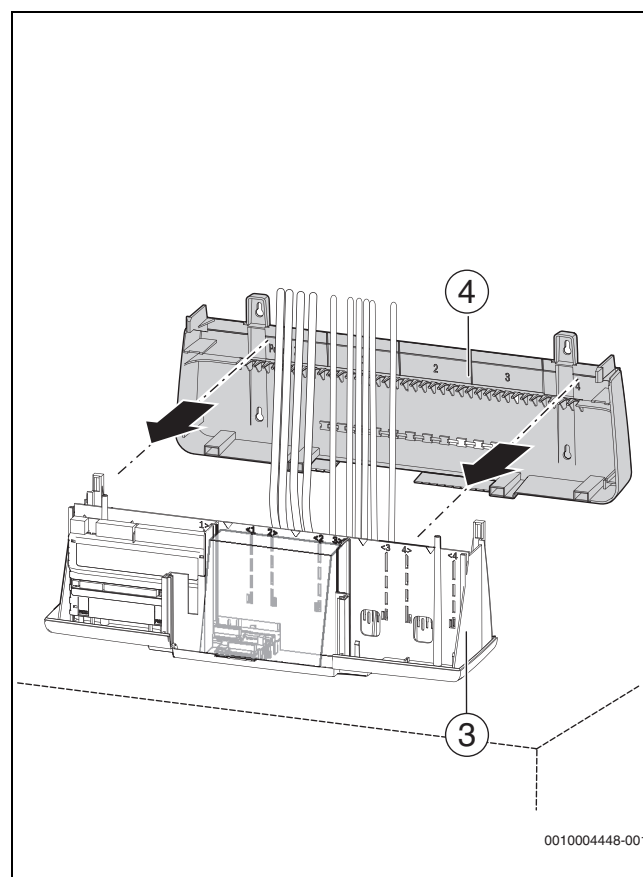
Insérer le montage dans la chaudière, enclencher le panneau arrière
